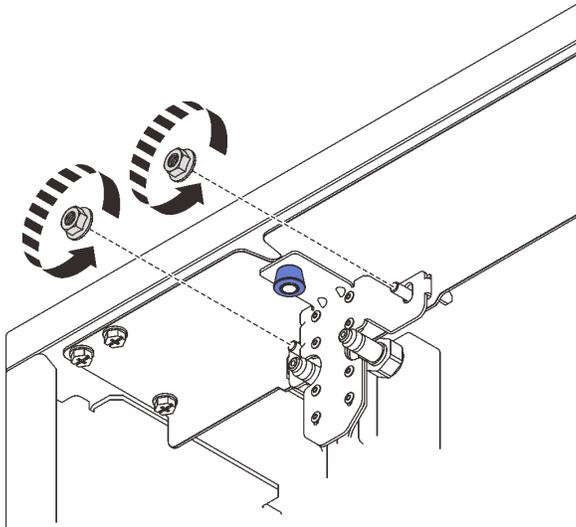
Entfernen der Muttern von der oberen Montagehalterung für die Rackleitung
